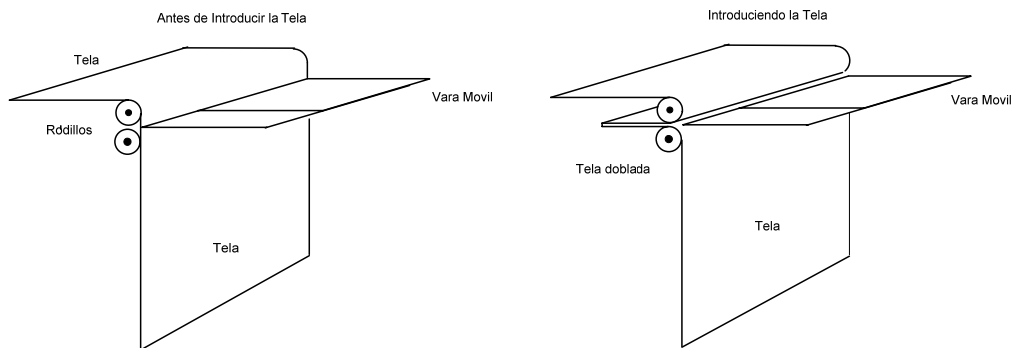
Sistema para doblar por rodillos y cuchilla
